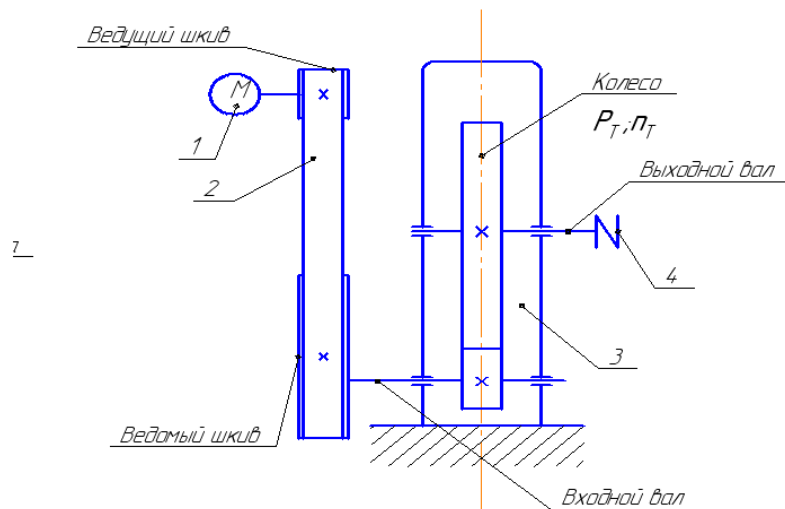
Кинематическая схема привода с ременной передачей и цилиндрическим редуктором
